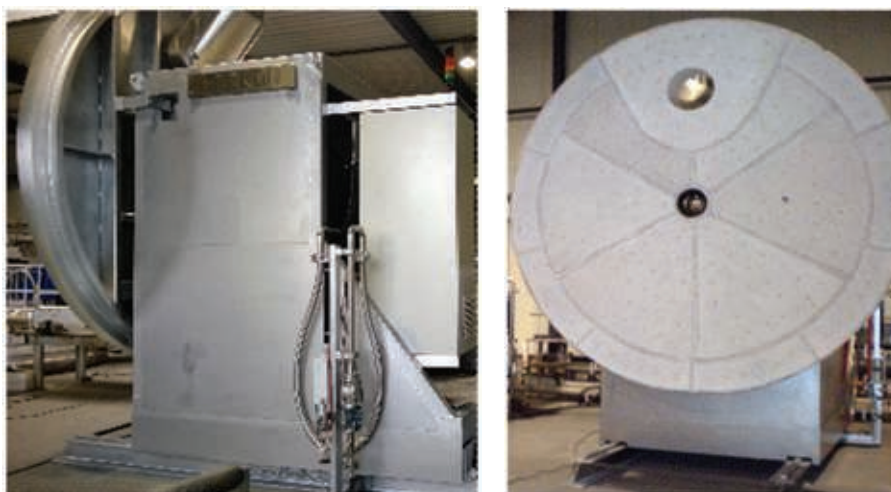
Горизонтальный стенд сушки и разогрева сталеразливочного ковша фирмы MEFCON
